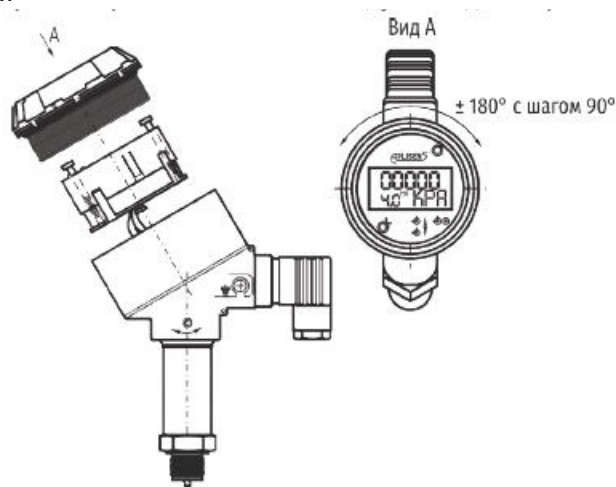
Преобразователь с исполнением корпуса ALW-TL
